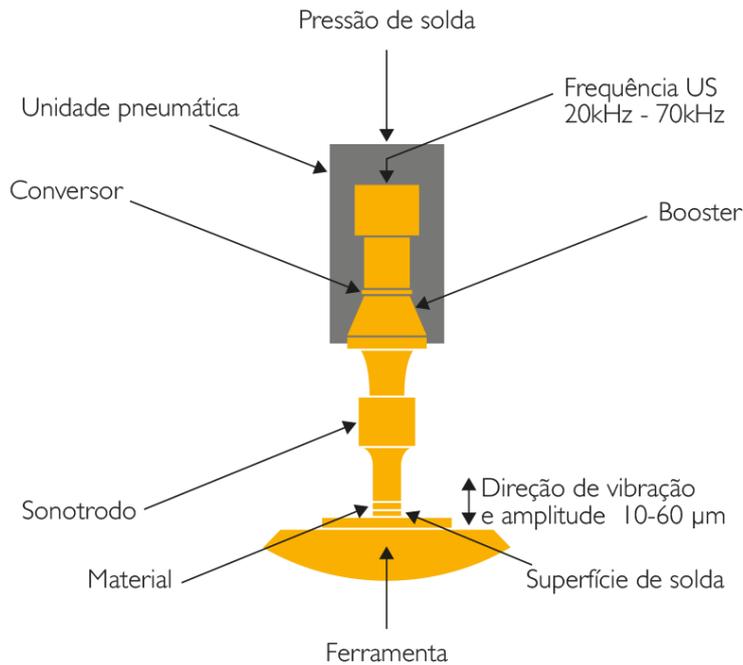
Esquema de soldagem por ultrassom. (Fonte: Cemas Eletra)
